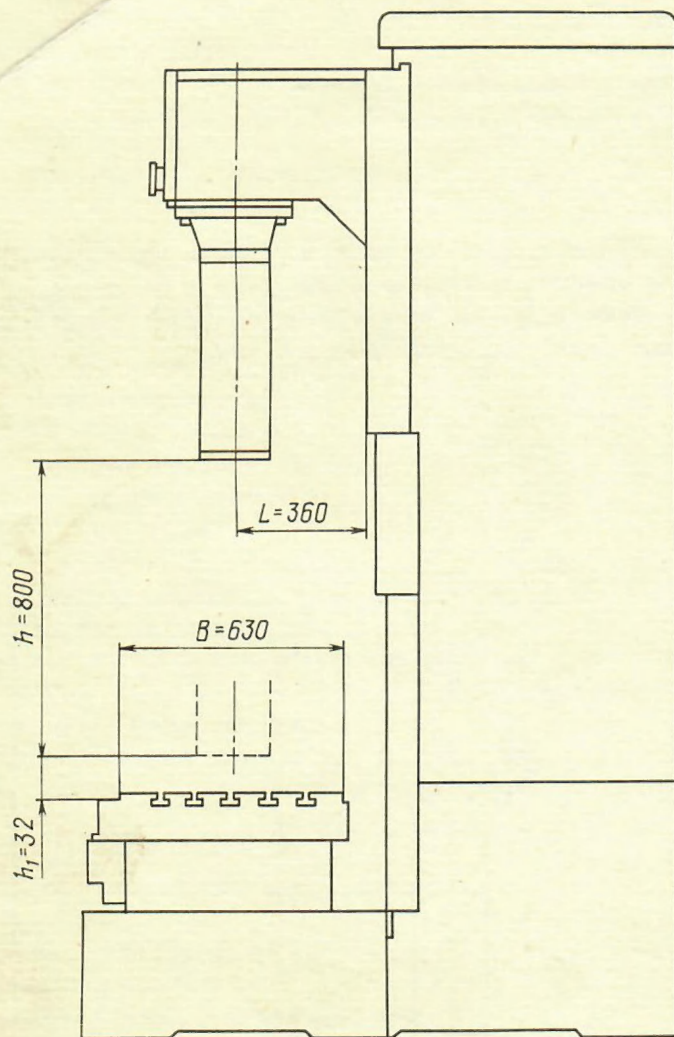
Габаритные размеры рабочего пространства станка 2733II
